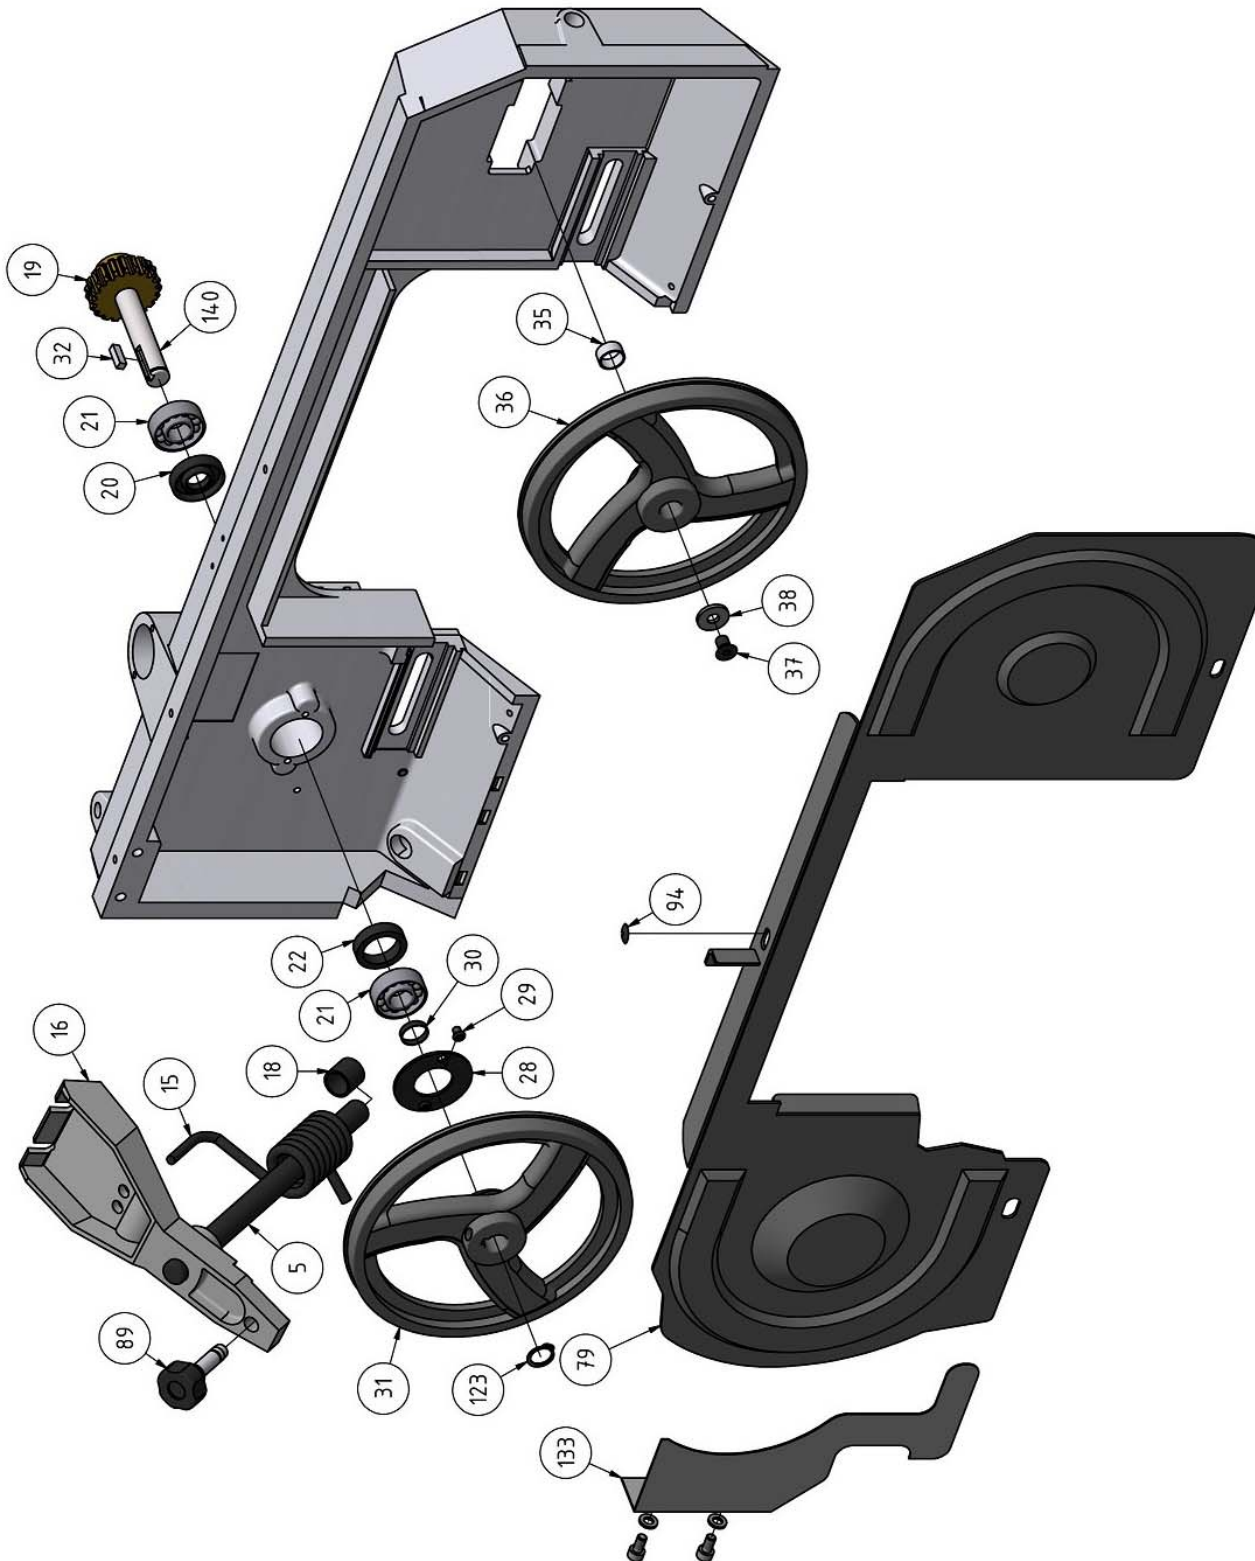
Ersatzteilzeichnung 2 von 4 - Parts drawing 2 of 4
